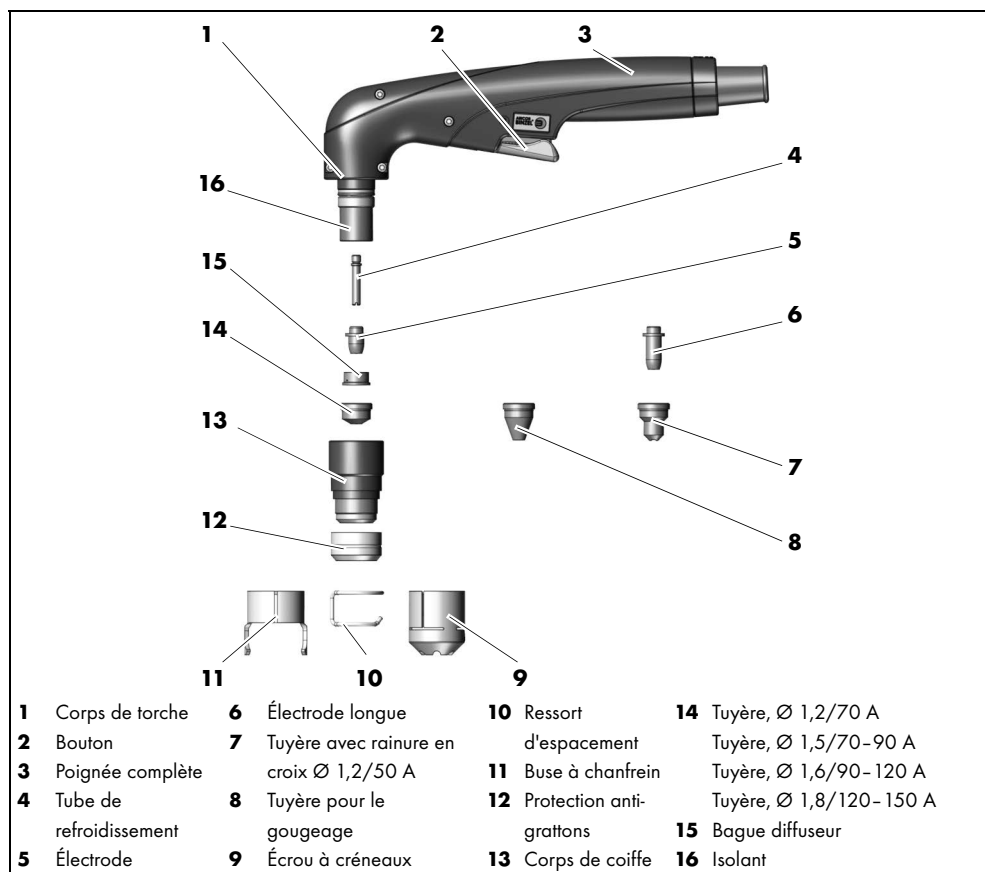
Vue d'ensemble d'ABIPLAS® CUT 151 HF
